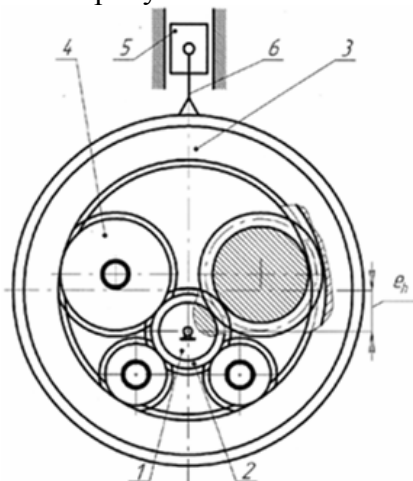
Зубчатый эксцентриковый подшипник (ЗЭП)
